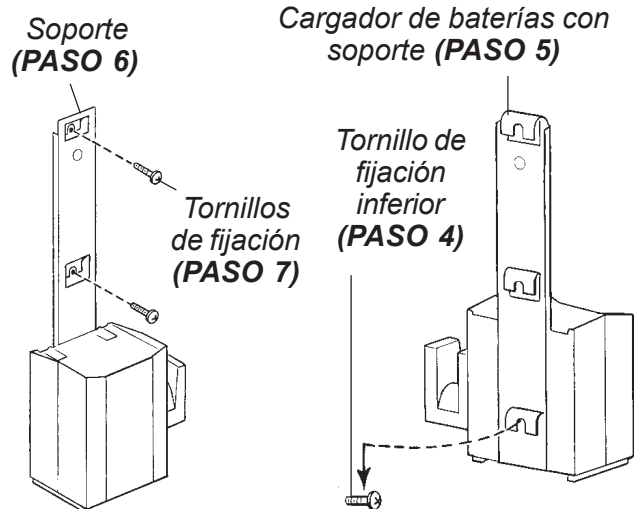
MONTAJE DEL CARGADOR DE BATERÍAS
